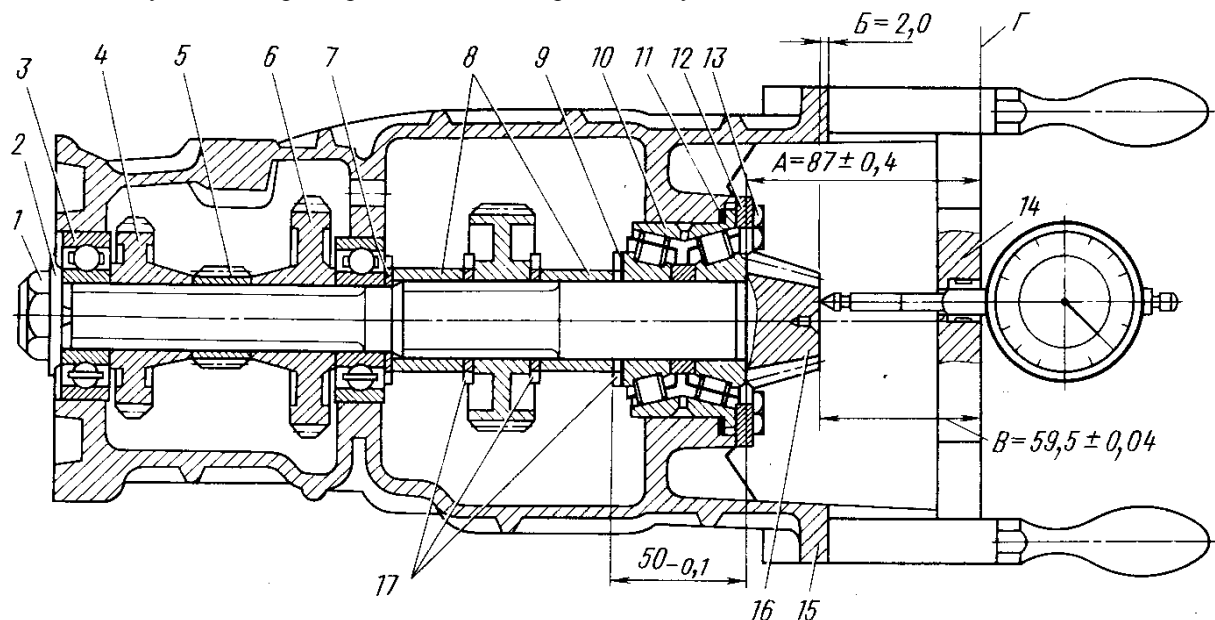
Установка ведущей шестерни главной передачи: 1 — гайка ведущего вала главной передачи; 2 — отгибная шайба; 3 — задний подшипник; 4 — ведомая шестерня IV передачи; 5 — ведущая шестерня привода спидометра; 6 — ведомая шестерня III передачи; 7 — упорная шайба ведомой шестерни II передачи; 8 — распорные втулки шестерен; 9, 11 — регулировочные прокладки; 10 — передний упорный подшипник; 12 — крышка подшипника; 13 — болт; 14 — контрольное приспособление для подбора толщины регулировочных шайб; 15 — картер коробки передач; 16 — ведущая шестерня главной передачи; 17 — упорные шайбы шестерен передач; Г — ось отверстия диаметром  $115^{0,035}$  мм.
